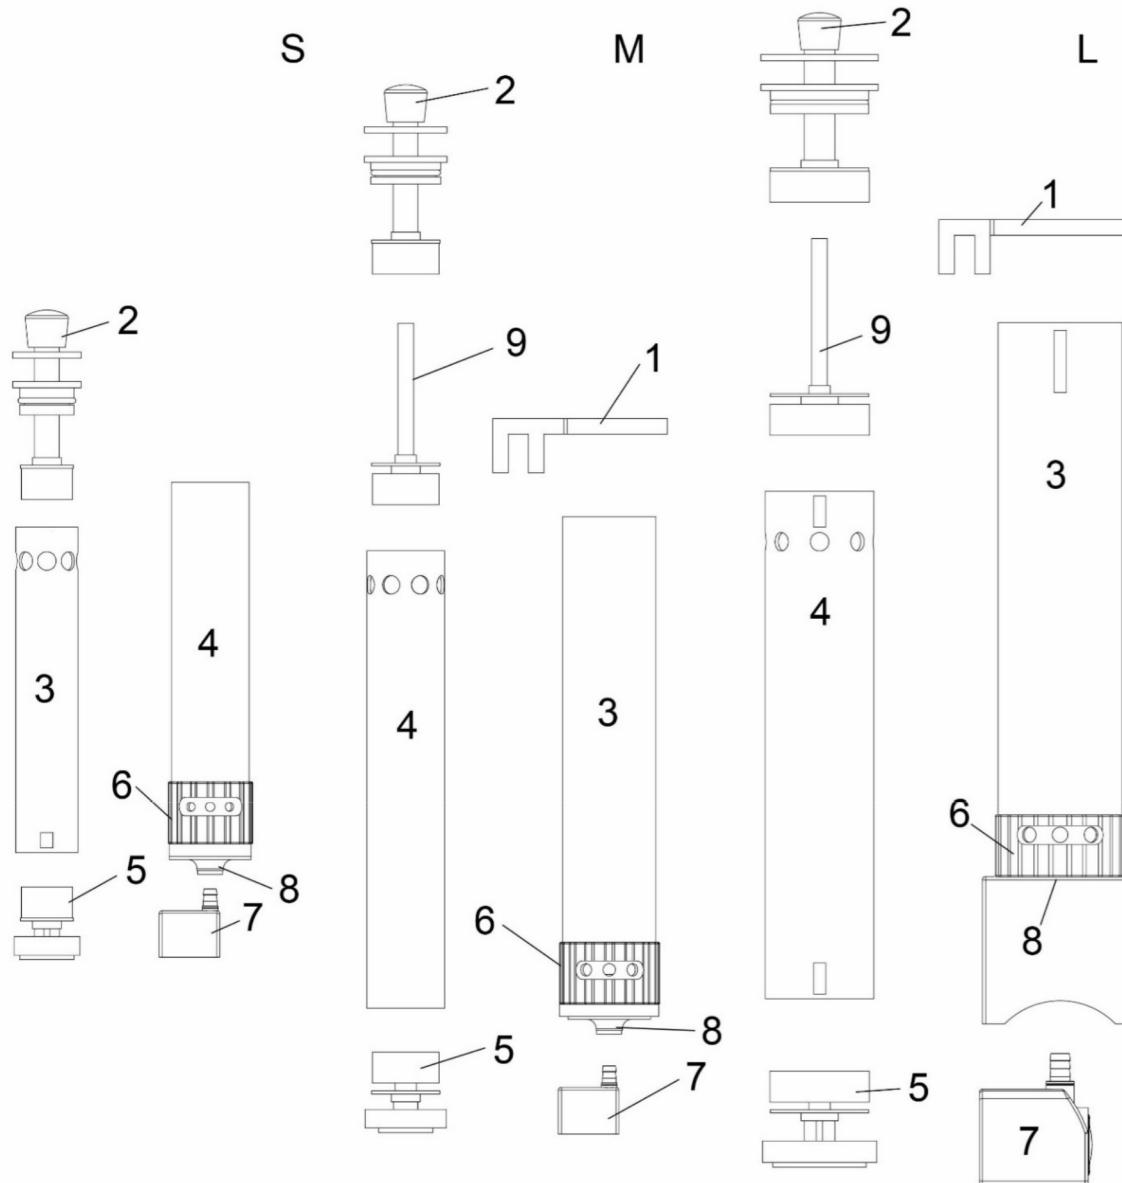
1. Unità di supporto 2. Maniglia rotante (regolatore di flusso) 3. Spugna 4. O-rings (S + M: 2 O-rings, L: 1 O-ring) 6. Uscita
